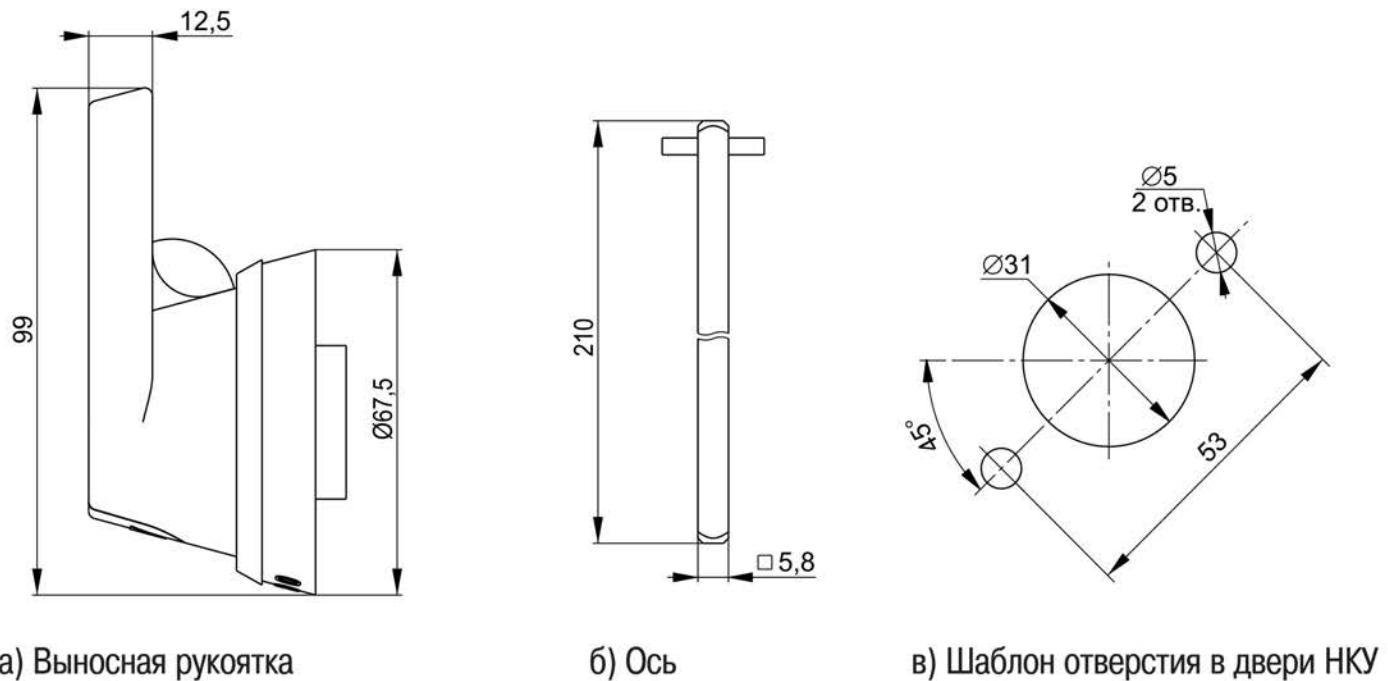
Габаритные и установочные размеры выносной рукоятки и оси
